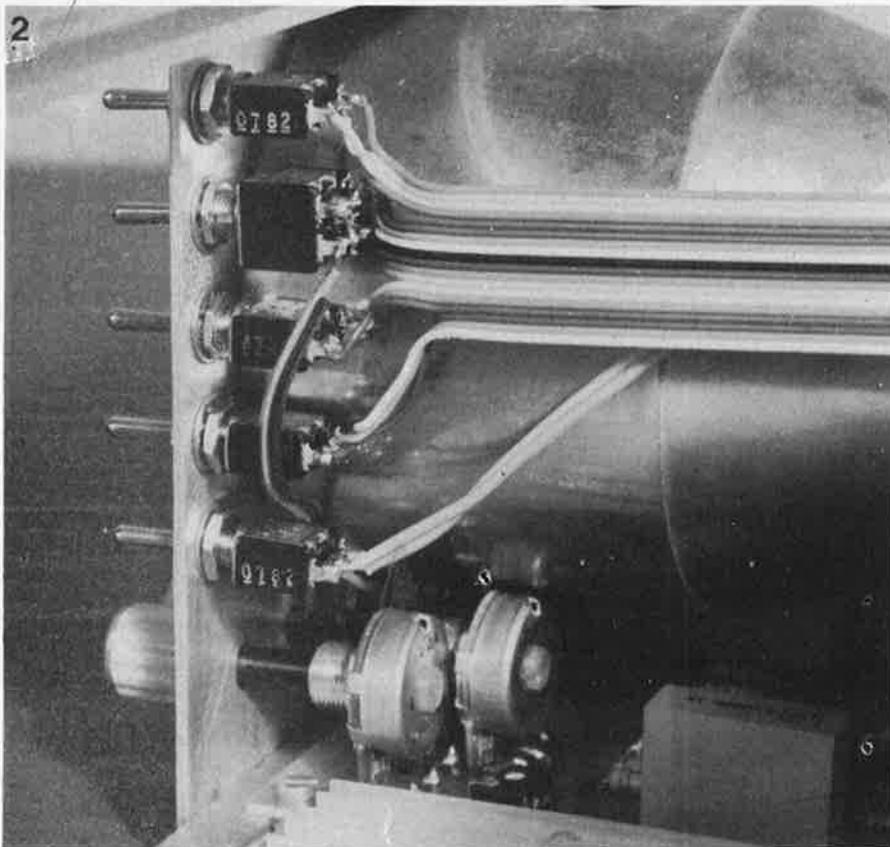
Vue de la face avant des 2 versions de l'Elektroscope.
